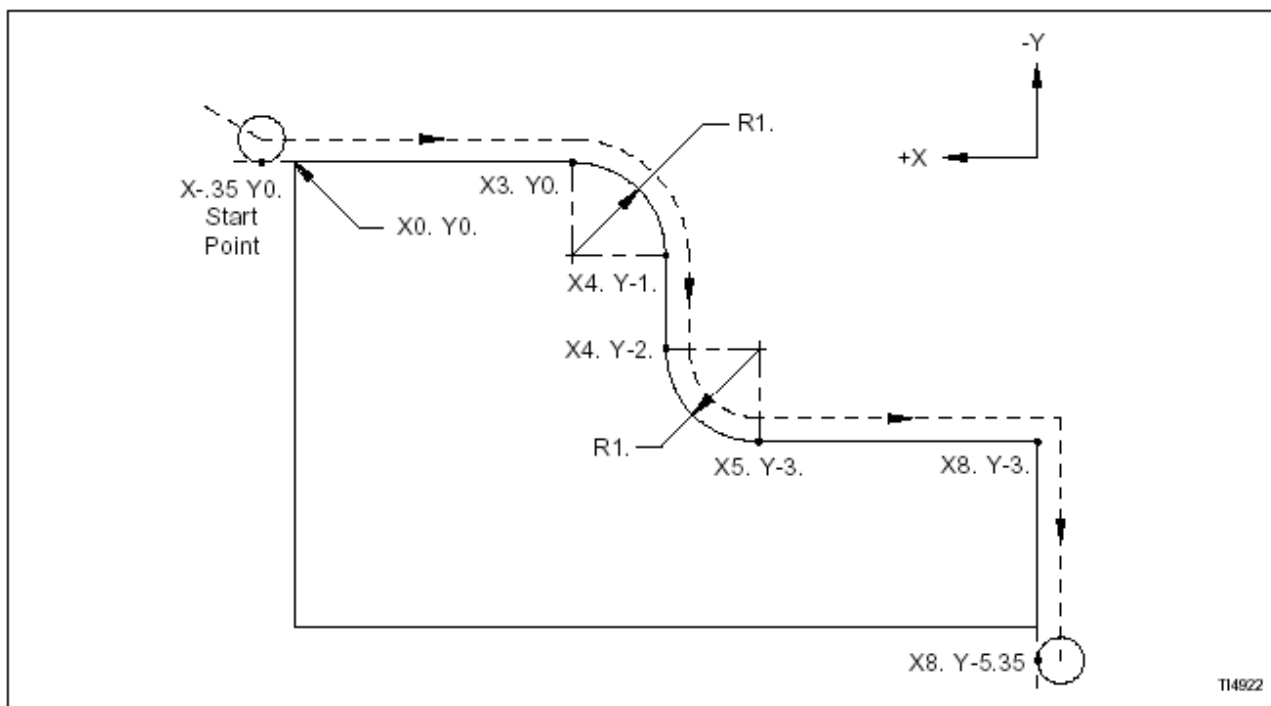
Контур заготовки для типовой программы обработки детали.
